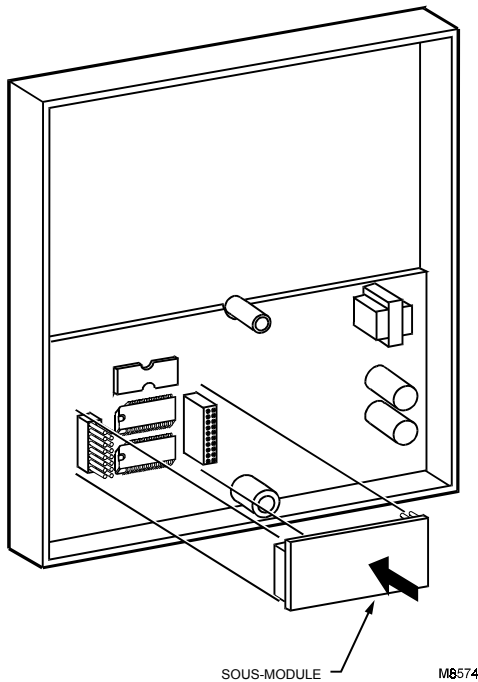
Mettre en place le sous-module et remonter le boîtier.
